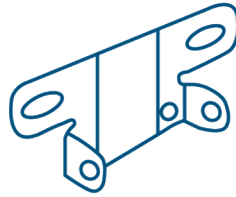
Torarm-Halterung, 1 Stk.
